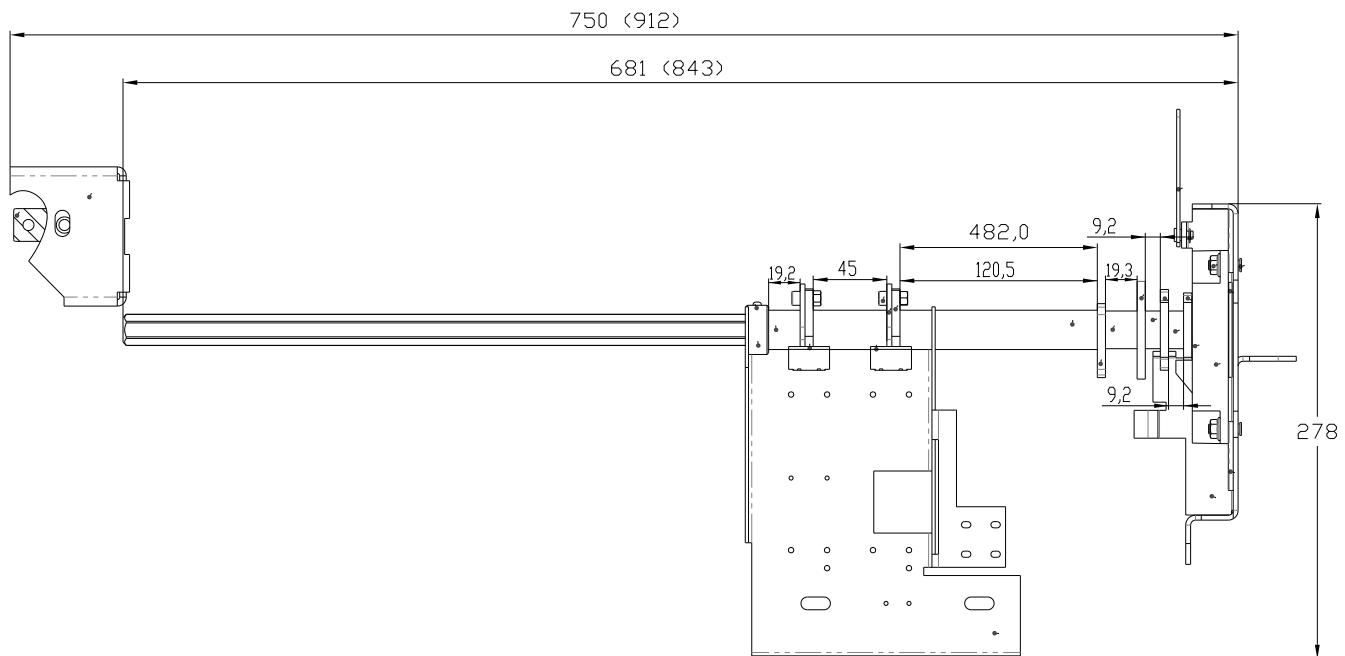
Габаритные размеры привода заземлителя с ручным управлением.
